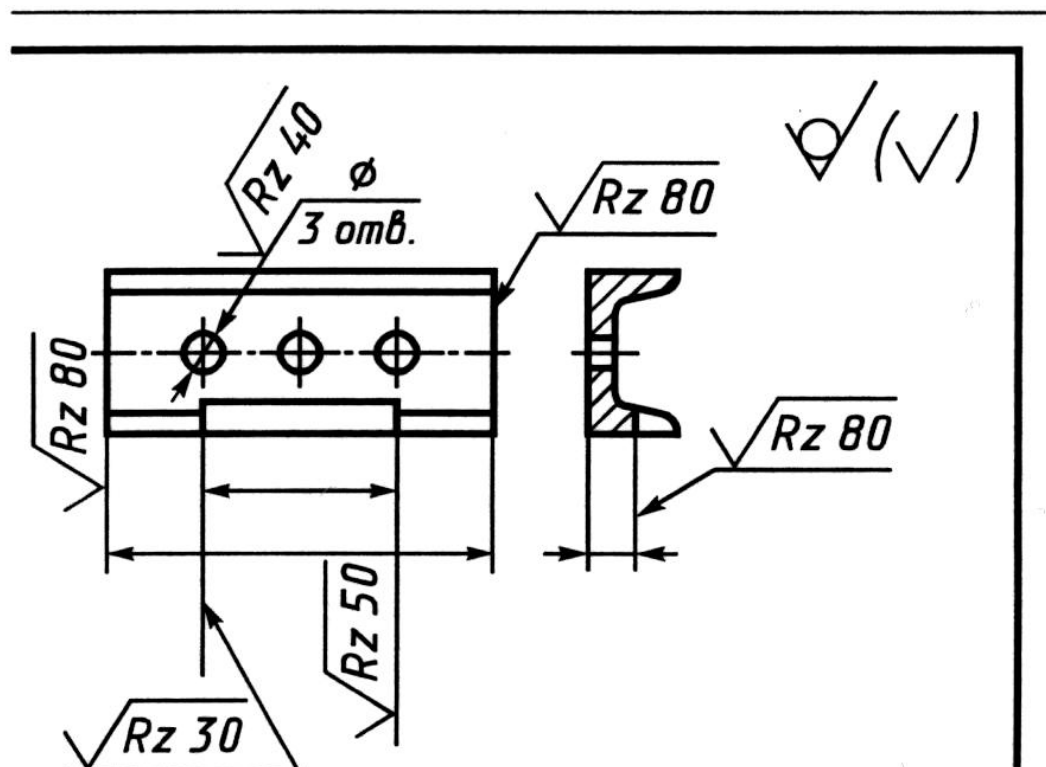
Обозначение шероховатости, одинаковой для части поверхностей изделия
